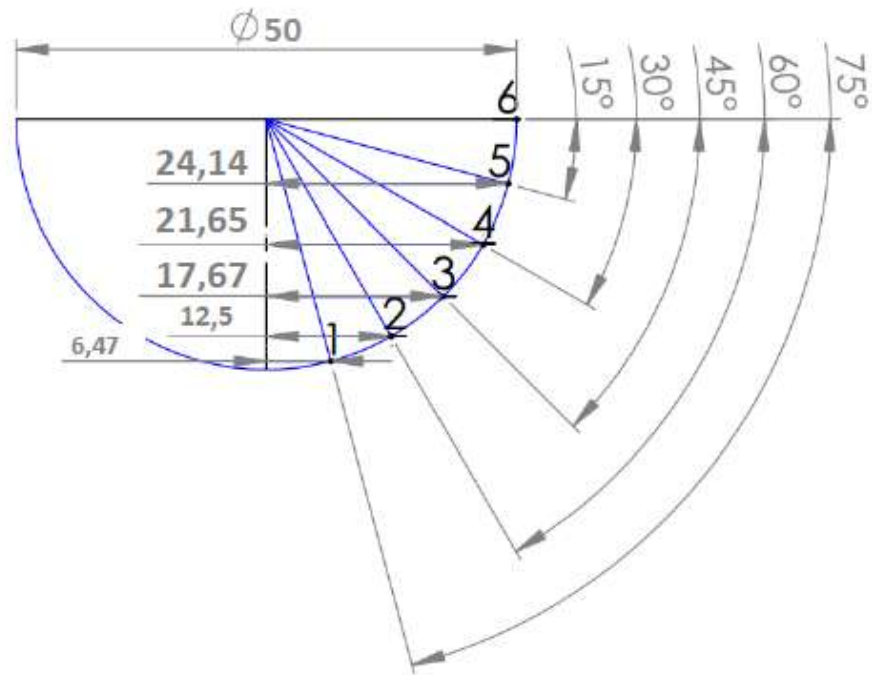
Радіуси обертання вертлюжної фрези в робочих точках термопар
